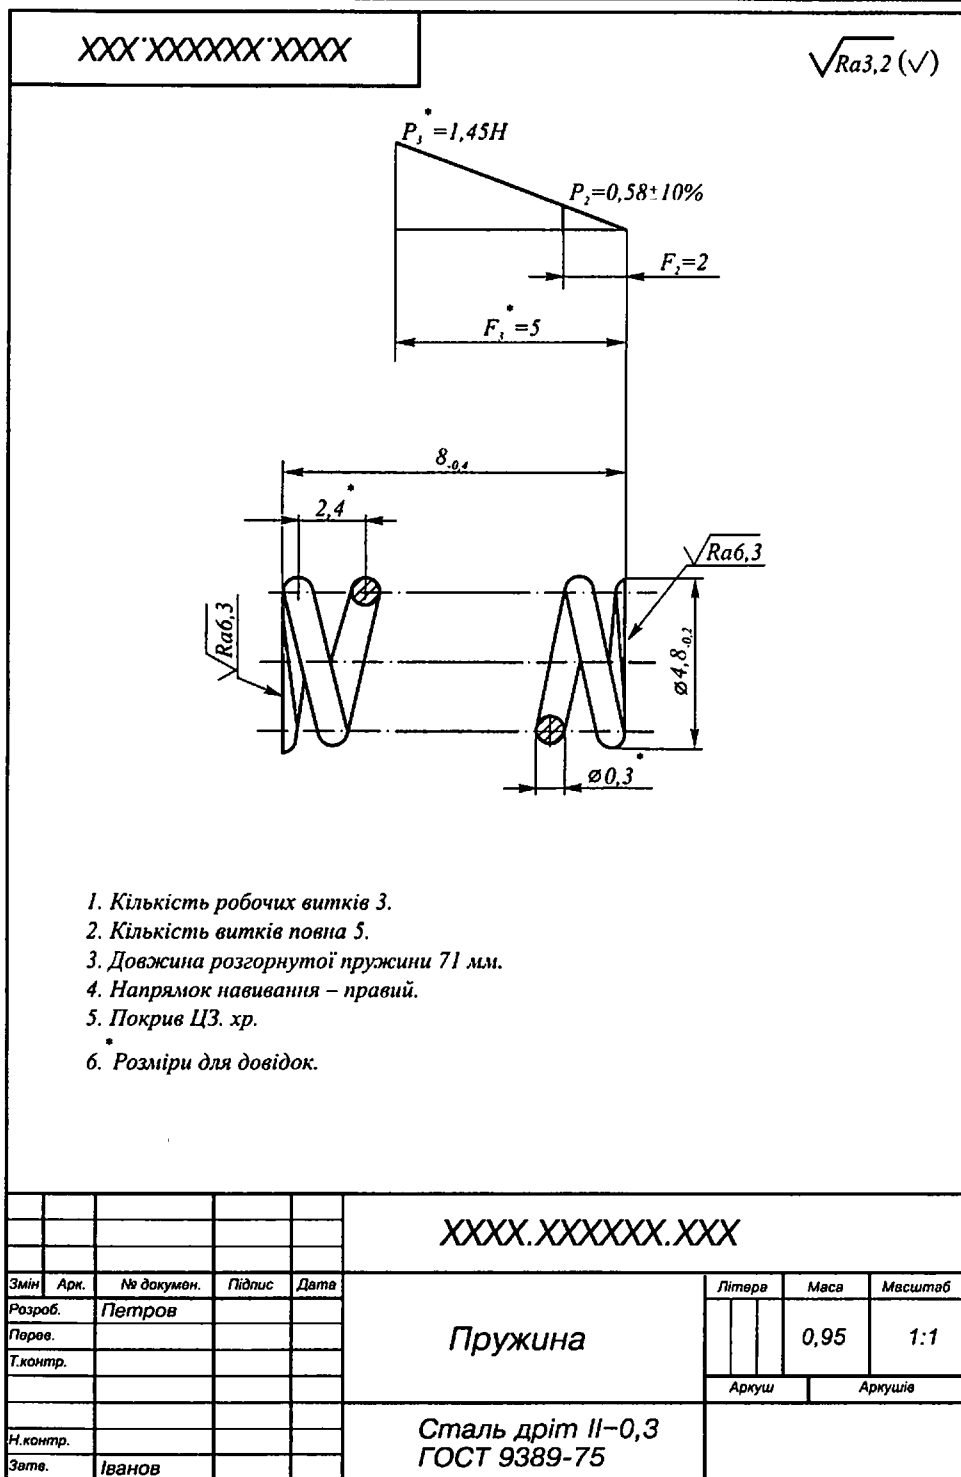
Робочий кресленик гвинтової пружини стиску
